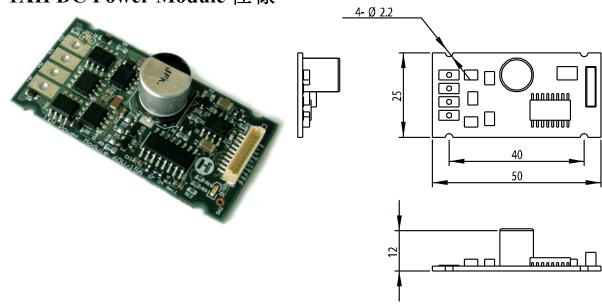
1XH DC Power Module の写真および寸法 1XH DC Power Module photo and dimensions
